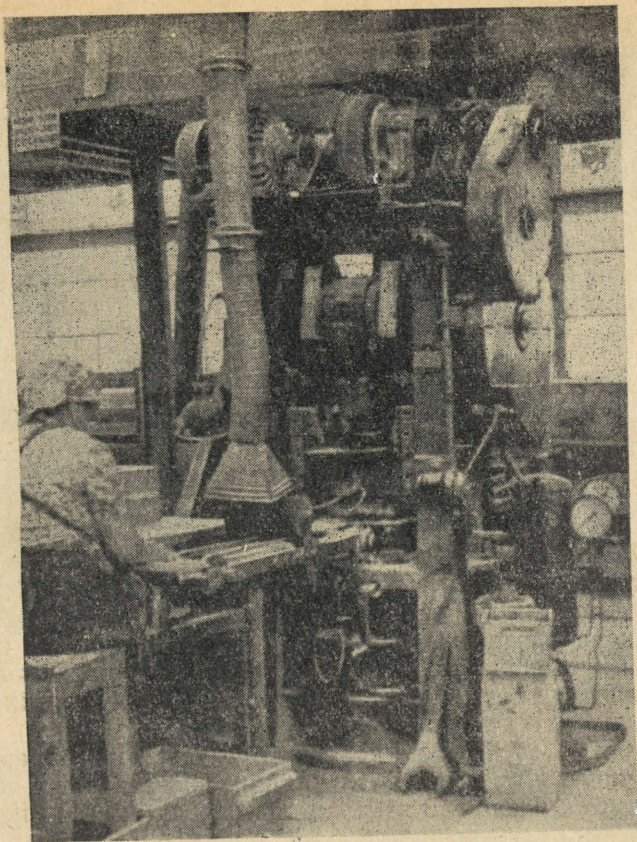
Коленчато-рычажный пресс для прессования облицовочных плиток.
